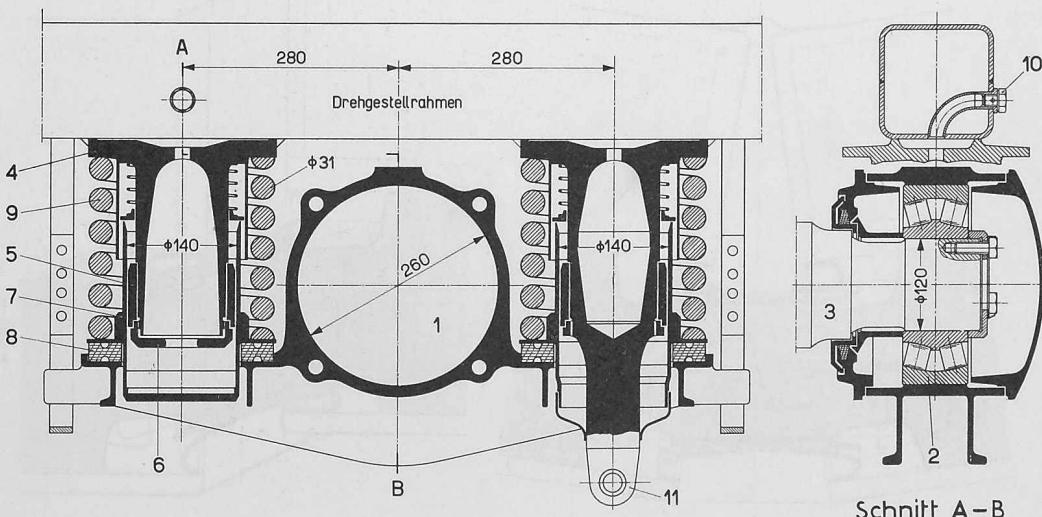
(links). Achslager-Führung und -Federung der Laufdrehgestelle
